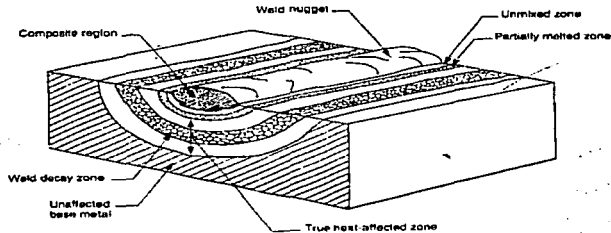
Esquema de la estructura de la soldadura [29].
